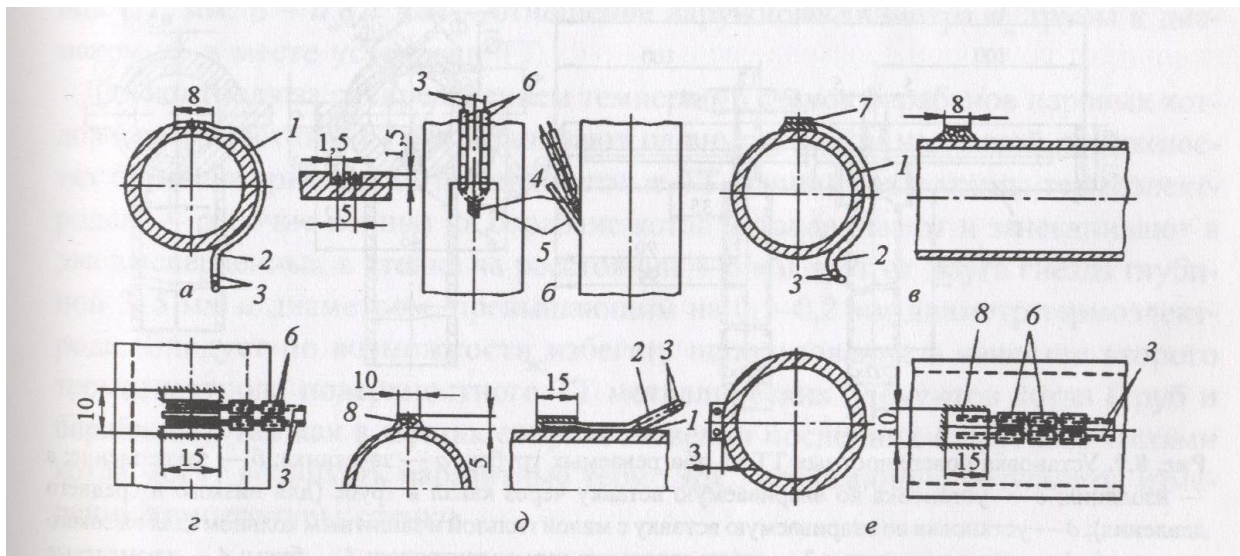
Установка поверхностных ТТ на не обогреваемых трубах: а – зачеканка в канавки, вырубленные в стенке трубы; б – зачеканка под стружку трубы; в – зачеканка в наплавленный бугорок металла; г – зачеканка в прорези приваренной бобышки; д, е – зачеканка в отверстия приваренной бобышки; 1 – слюда; 2 – изоляция; 3 – термоэлектроды; 4 – рабочий конец термопары; 5 – стружка; 6 – бусы; 7 – бугорок; 8 – бобышка;
